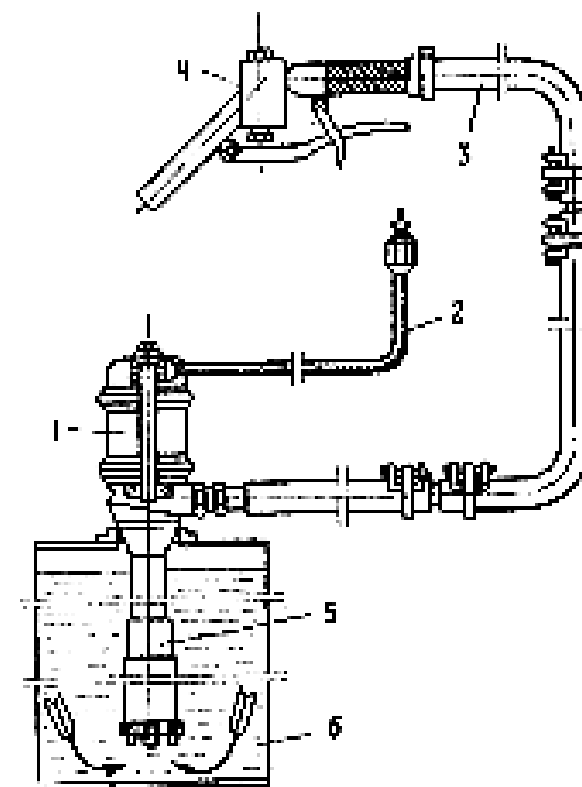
Малогабаритный заправочный агрегат МЗА-3:
